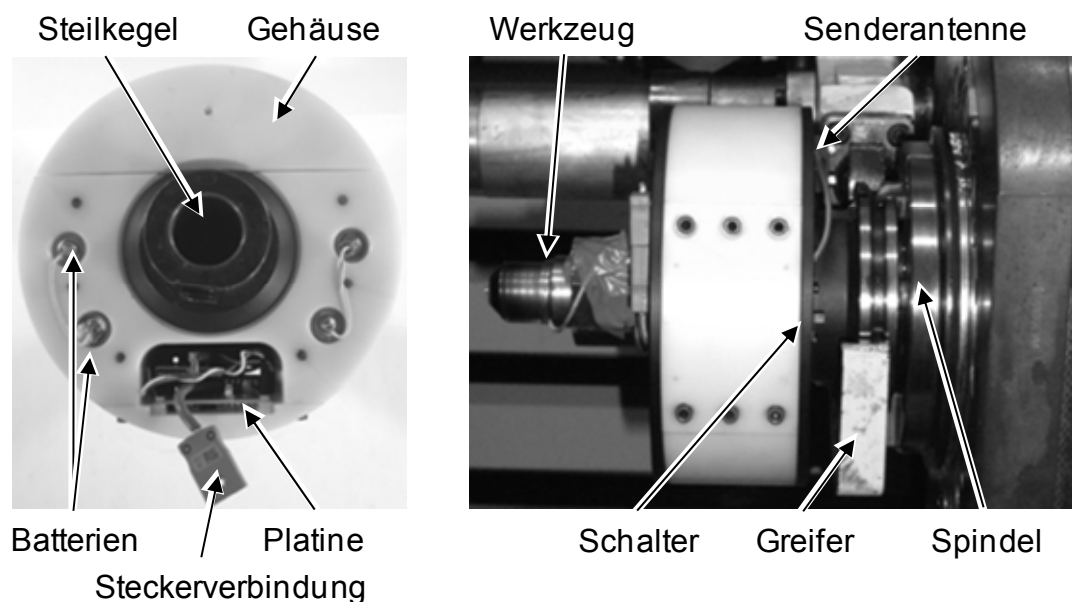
Werkzeughalter ohne (a) und mit eingesetztem FSW-Werkzeug (b) zur Messung der Werkzeugtemperatur
